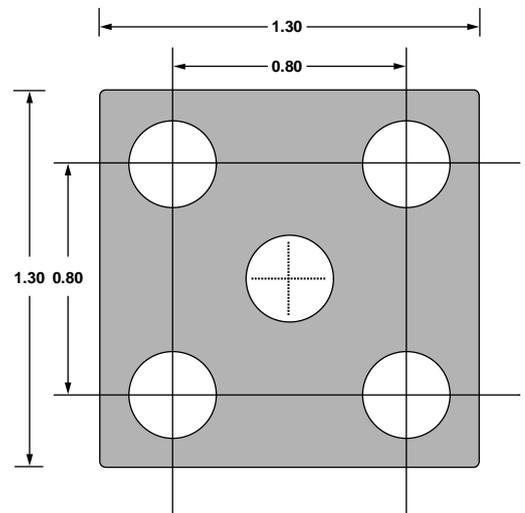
PCB サーマル・アタッチ・パッドの推奨寸法(mm)
